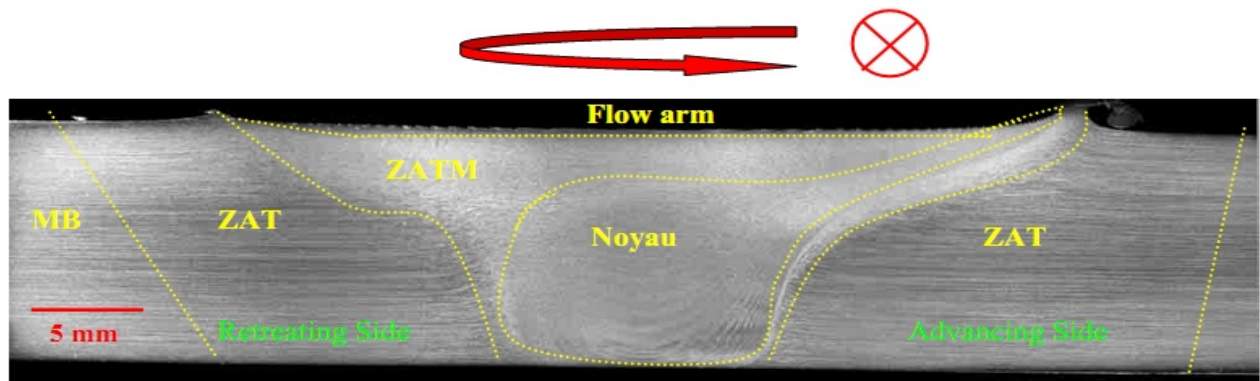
Coupe macrographique d'un joint soudé par FSW sur un alliage d'aluminium
